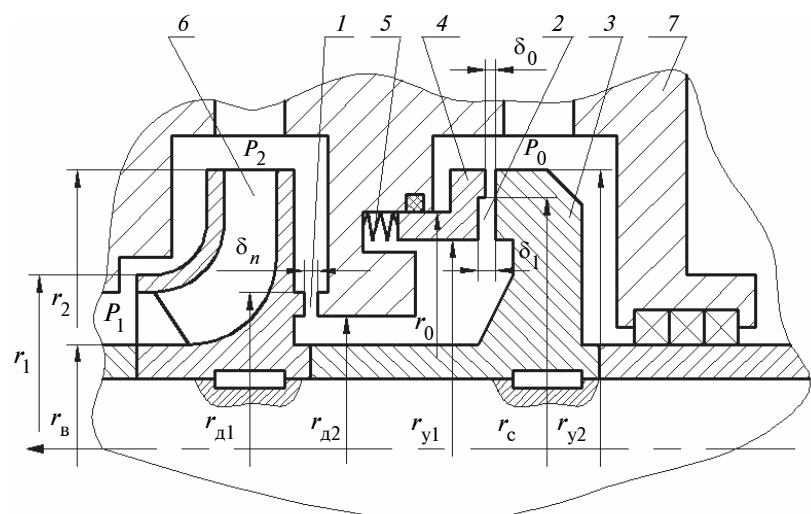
Розрахункова схема дроселюючого бар'єра: 1, 2 – торцеві дроселі; 3 – розвантажувальний диск; 4 – рухливе кільце; 5 – пружина; 6 – робоче колесо; 7 – корпус насоса
